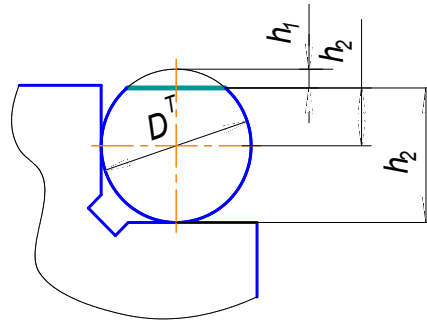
Схема образования погрешностей базирования размеров заготовки при ее установке в призму
